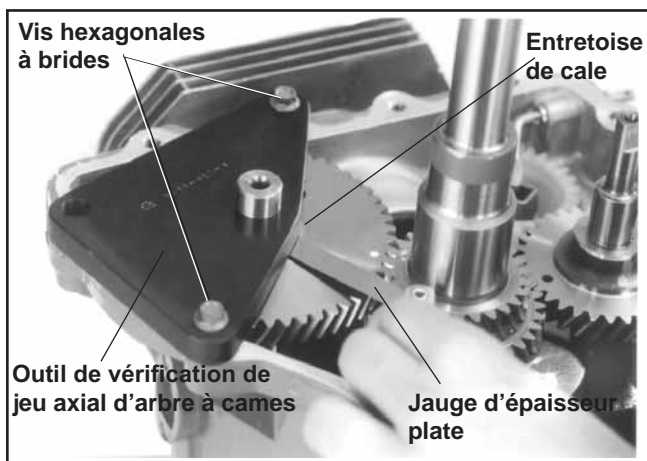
Contrôle du jeu axial de l'arbre à cames.
